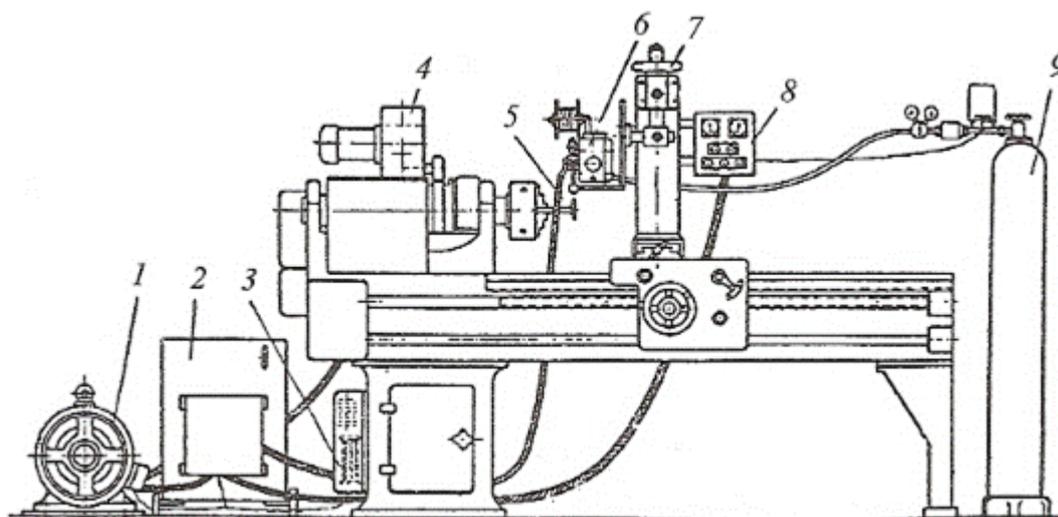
Установка для газозлектрической наплавки; 1 — преобразователь ЗП—7,5/30; 2— аппаратный ящик; 3— реостат возбуждения; 4— привод станка; 5— наплавляемая деталь; 6— наплавочный аппарат; 7 — вертикальный суппорт;
